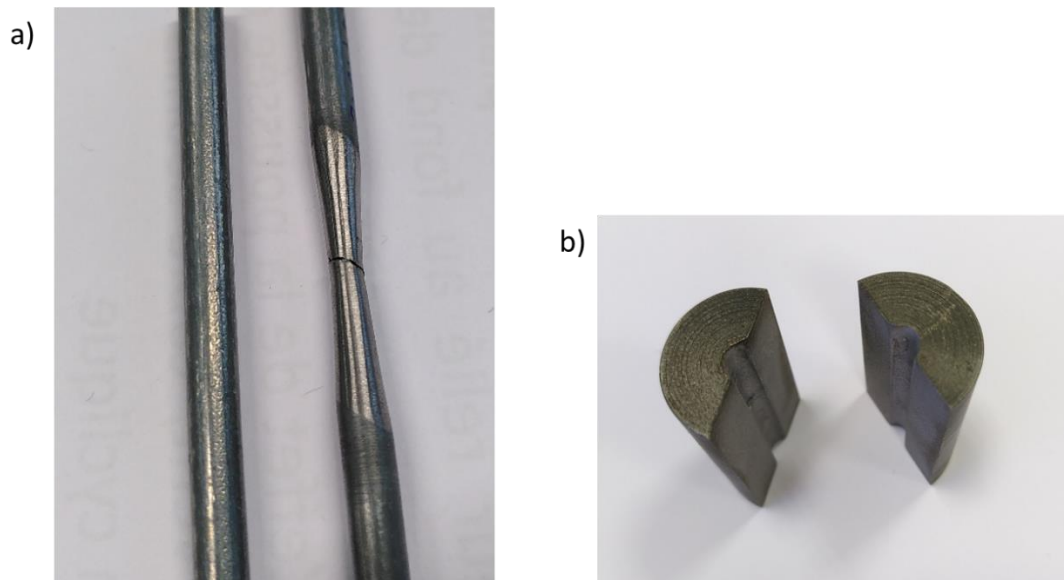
a) éprouvettes de traction avant et après usinage, b) "demi-coquilles" pour adaptation des mors aux éprouvettes
